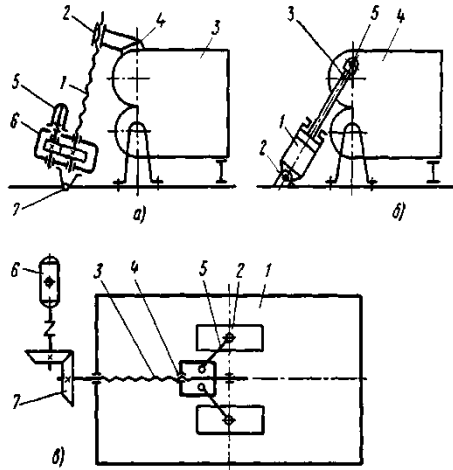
Схема механізму розвантаження змішувача:
